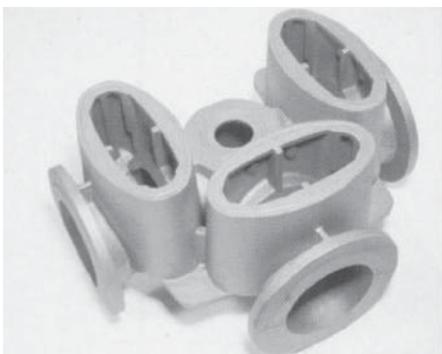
Некоторые примеры серийных отливок [отливки для узлов формовочных машин, отливки корпусов, обработанные и в сборе, толщина стенки от 8 до 80 мм]
